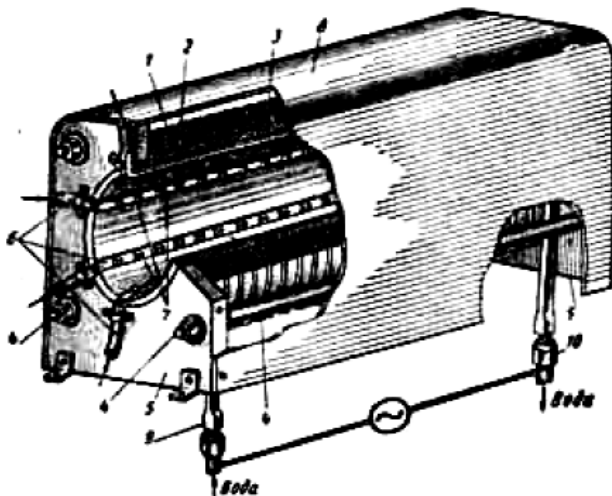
Схема индуктора для нагрева цилиндрических заготовок под ковку и штамповку
